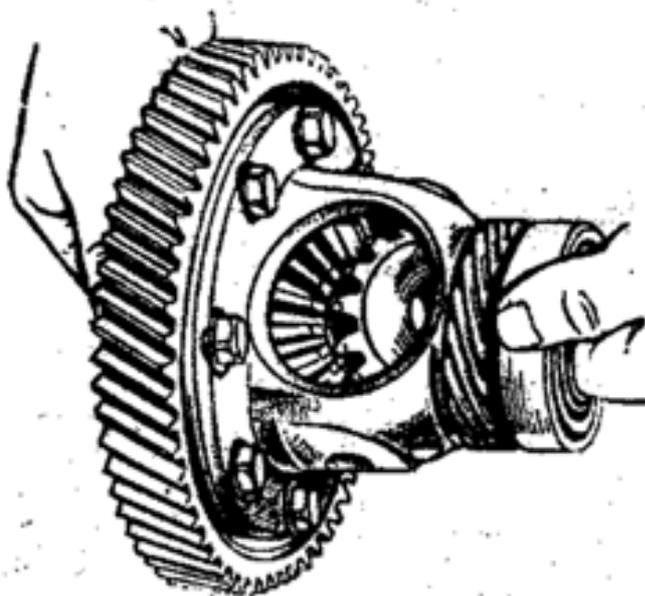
Выкатывание шестерен полуоси из коробки дифференциала
